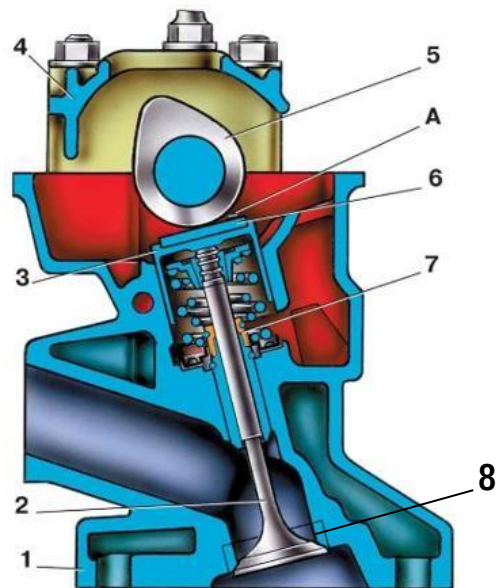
Схема клапанного sprzęження автомобільного двигуна: 1 – головка циліндрів; 2 – клапан; 3 – штовхач; 4 – корпус підшипників розподільного вала; 5 – розподільний вал; 6 – регулювальна шайба; 7 – маслоснімний ковпачок; 8 – сідло клапана; А – зазор між кулачком і регулювальною шайбою
